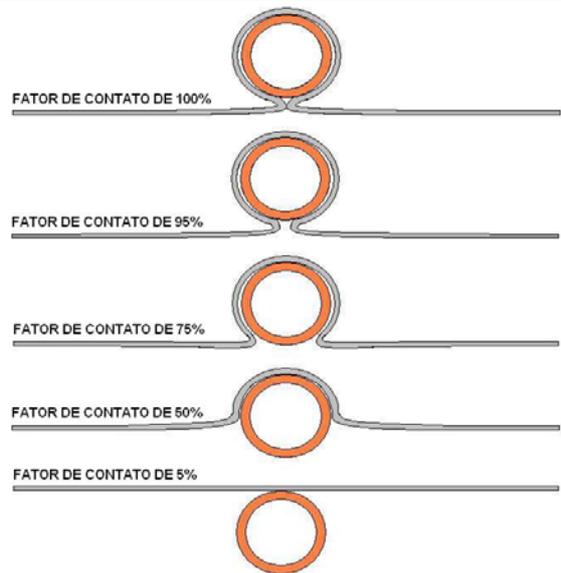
Exemplos de fator de contato entre Placa Absorvedora e Serpentina.
